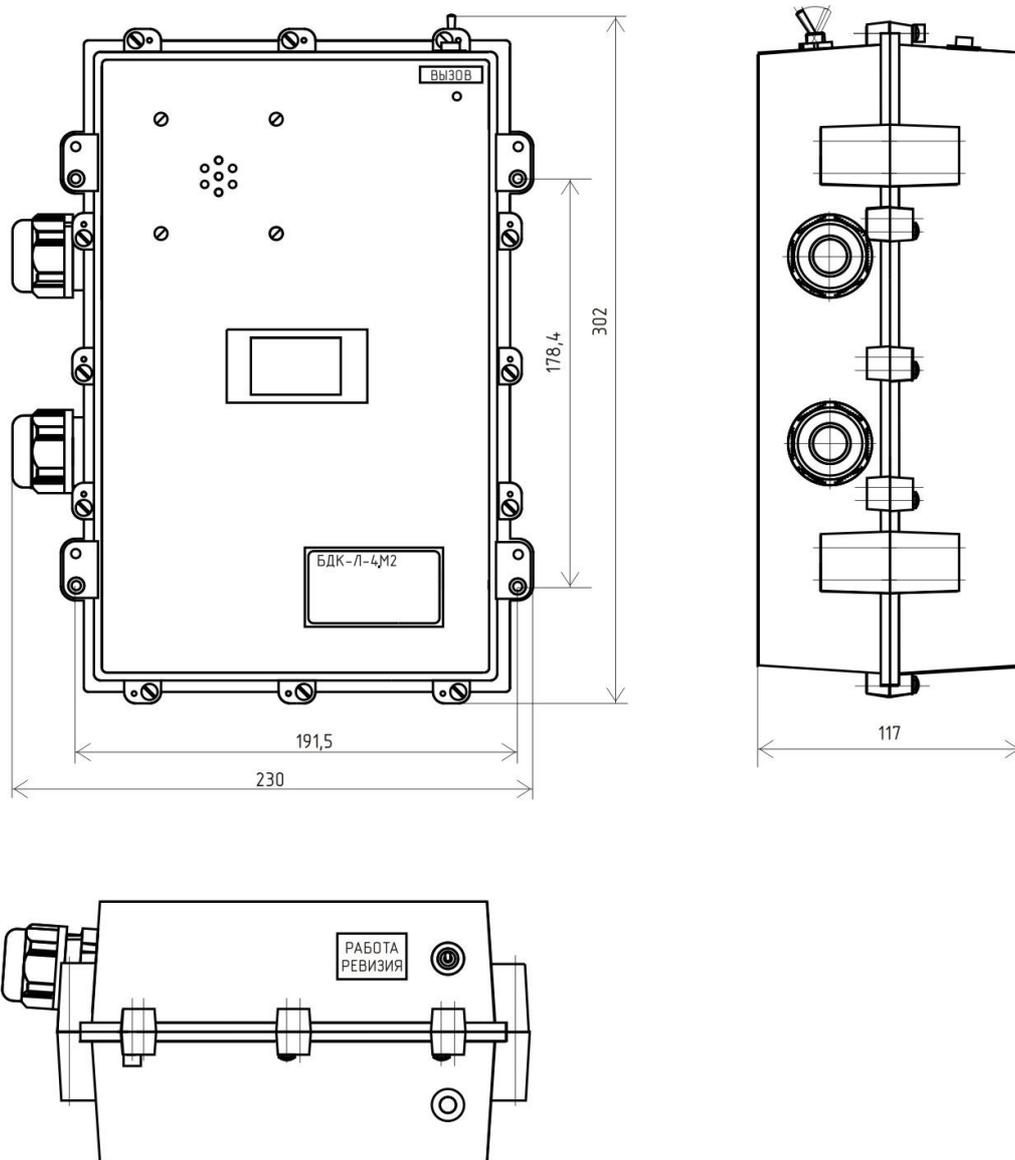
Габаритные размеры БДК-Л-4М2
